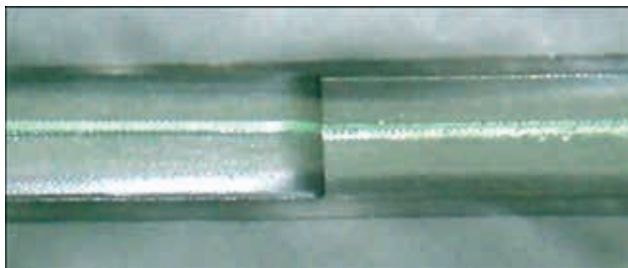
Зварний шов ламінованої тканини Unisol 950, виготовлений з недостатнім нагрівом зони зварювання
